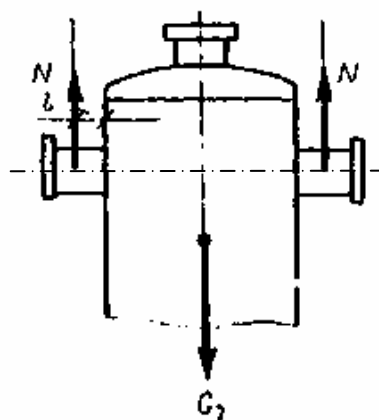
Схема к расчёту монтажных штуцеров
